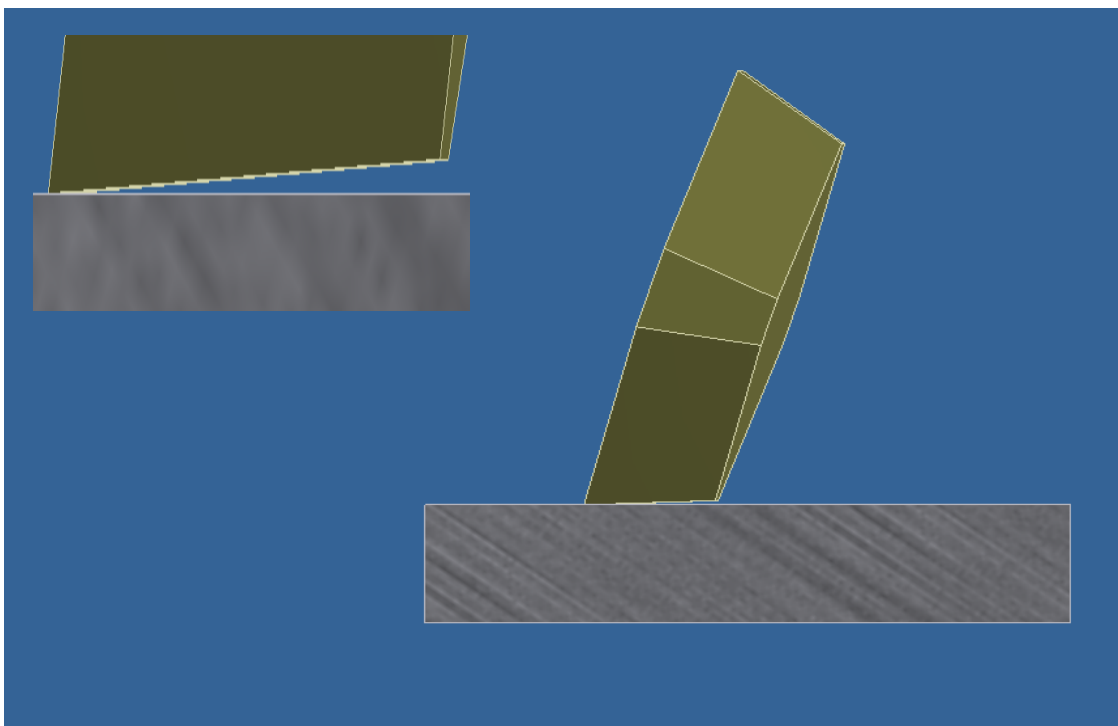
čelní fréza pozitivní geometrie [7]
